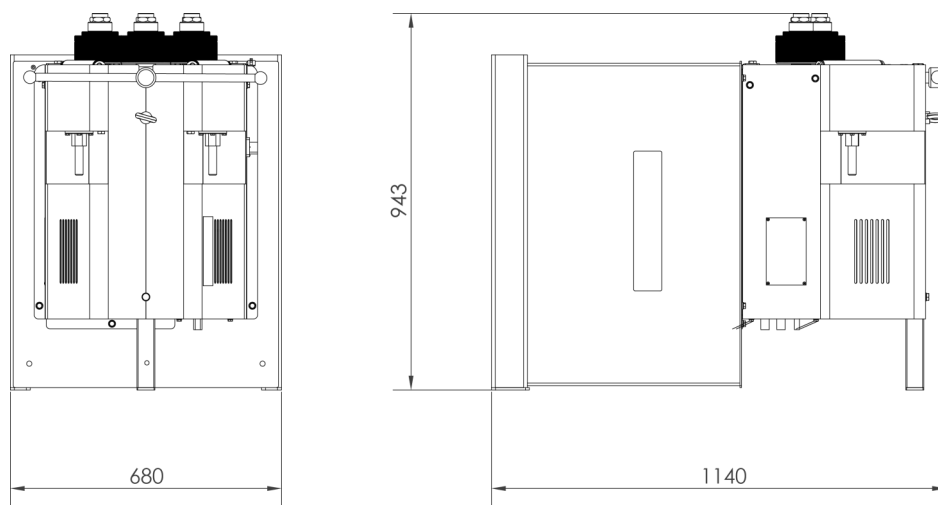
Dimensiones de la máquina con la bancada en posición horizontal
